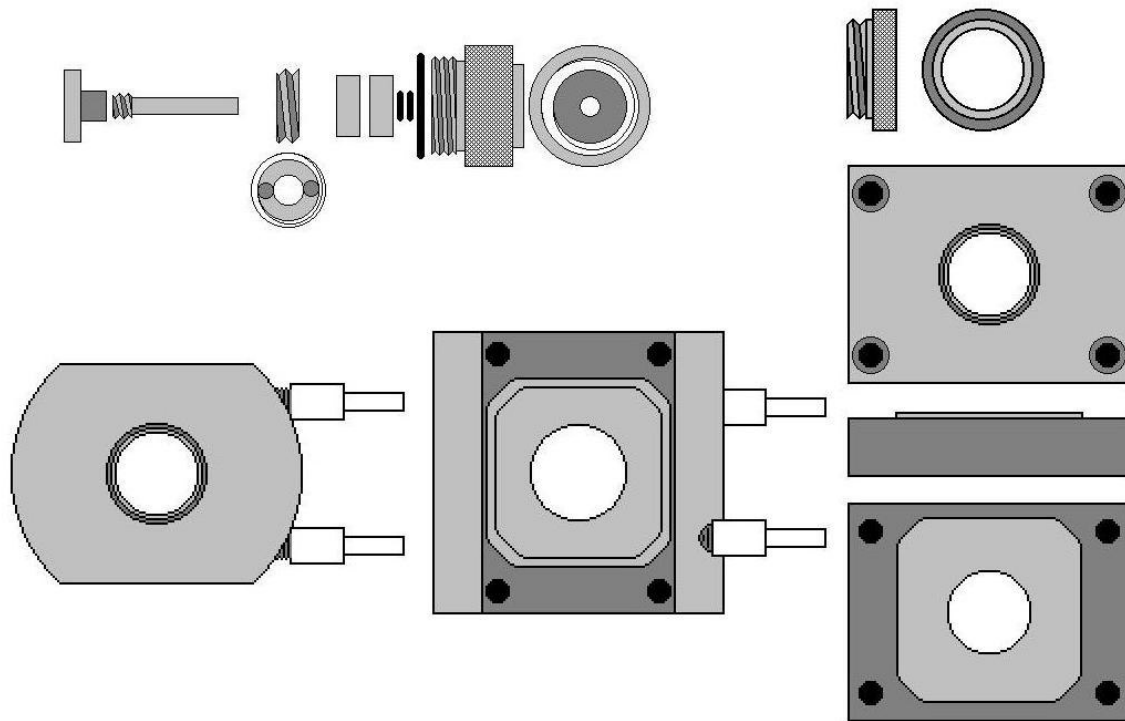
Diseño de un soporte para maquinado de cristales de carbón
